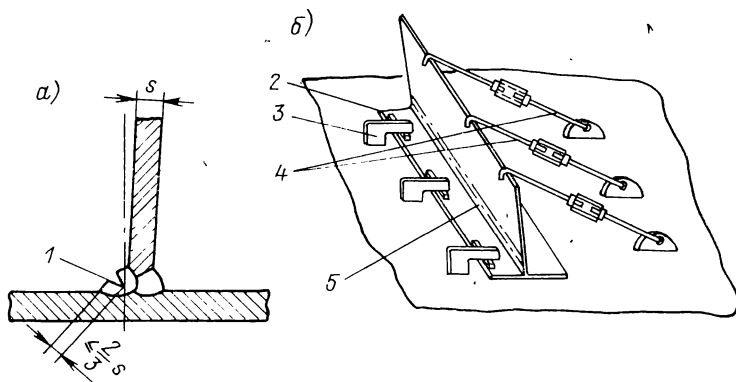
Схема правки завала стенки сварной тавровой балки: а) — наложением сварного шва по предварительно выстроганной канавке; б) — нагревом с упругим отгибом стенки.
